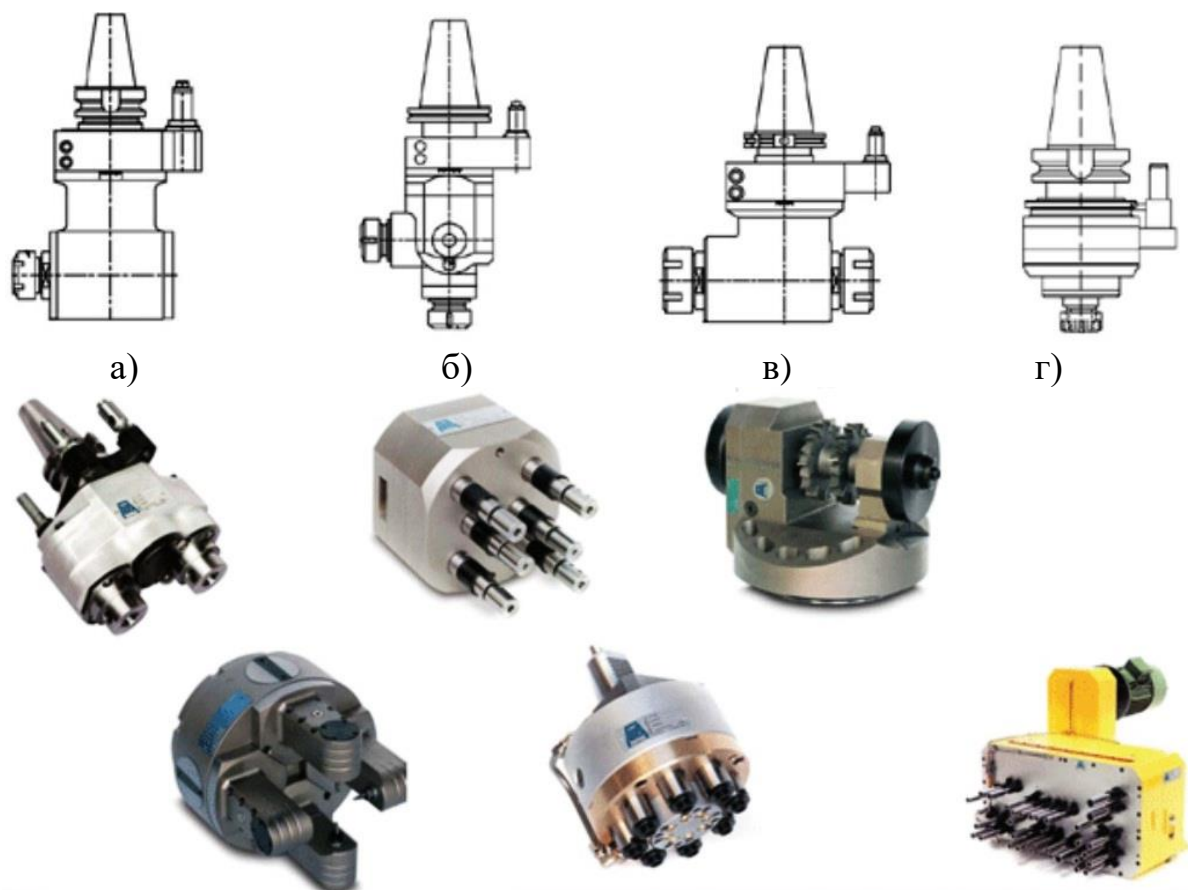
Приводний інструмент для верстатів фрезерної групи з ЧПК: центральний цанговий держак (а); поворотний цанговий держак (б); радіальний цанговий мультіплікаторний держак (в); прискорювальна головка (г); загальний вигляд
